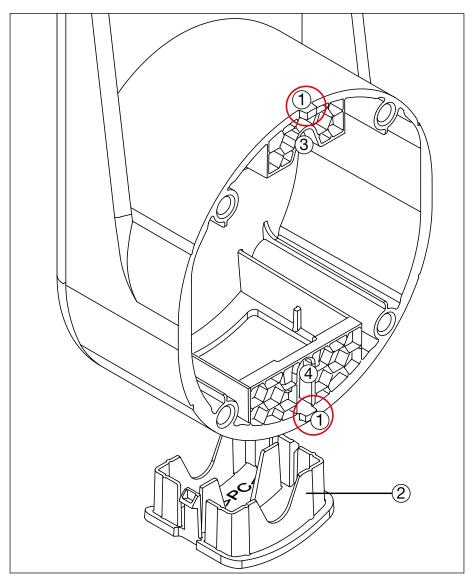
Montagem do suporte para cabos à parede (vista de trás)
